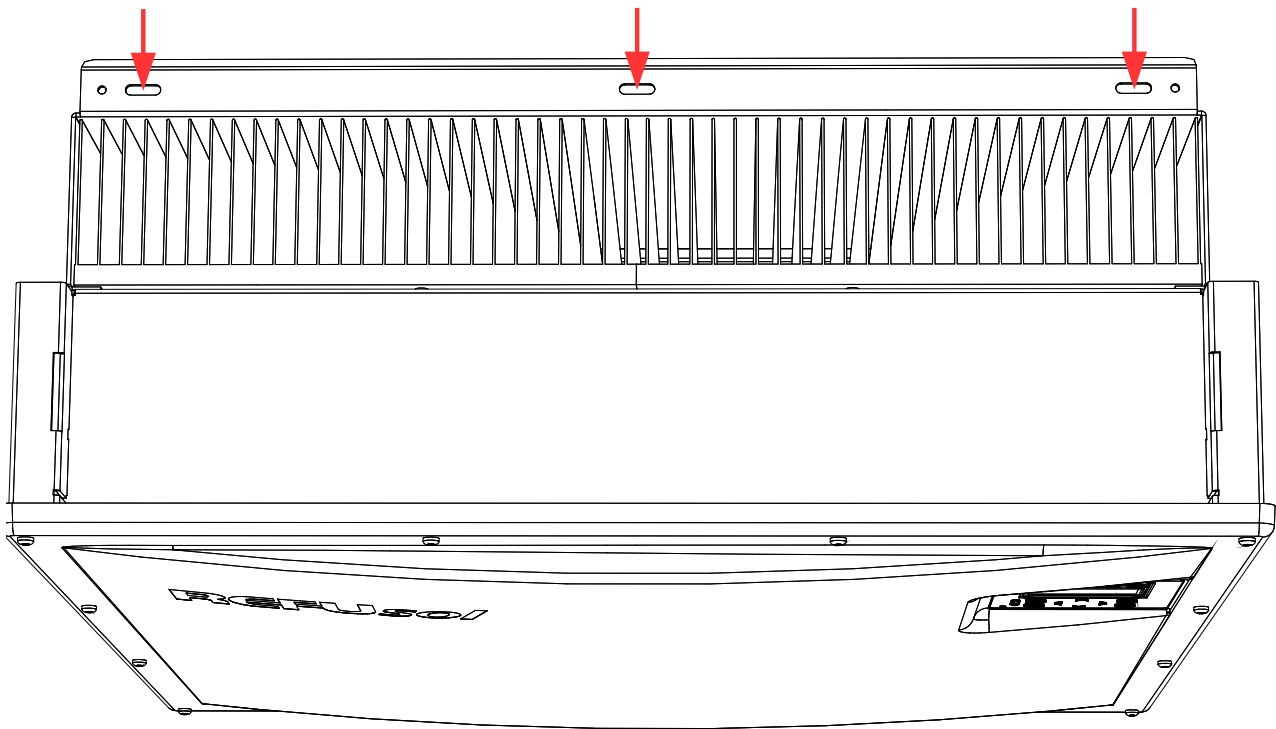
Mit 3 Schrauben befestigen (rote Pfeile)
